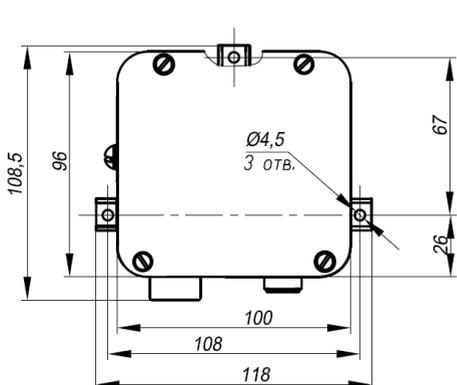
Присоединительные размеры датчика в силуминовом корпусе
